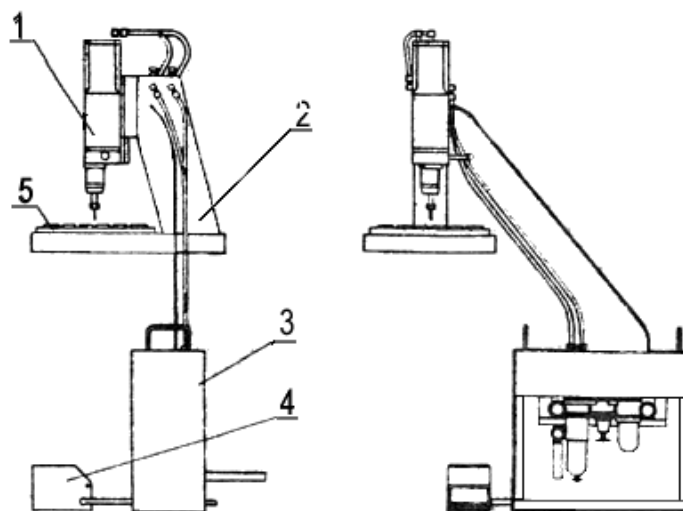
Общий вид одношпиндельного резьбонарезного станка модели HCA
